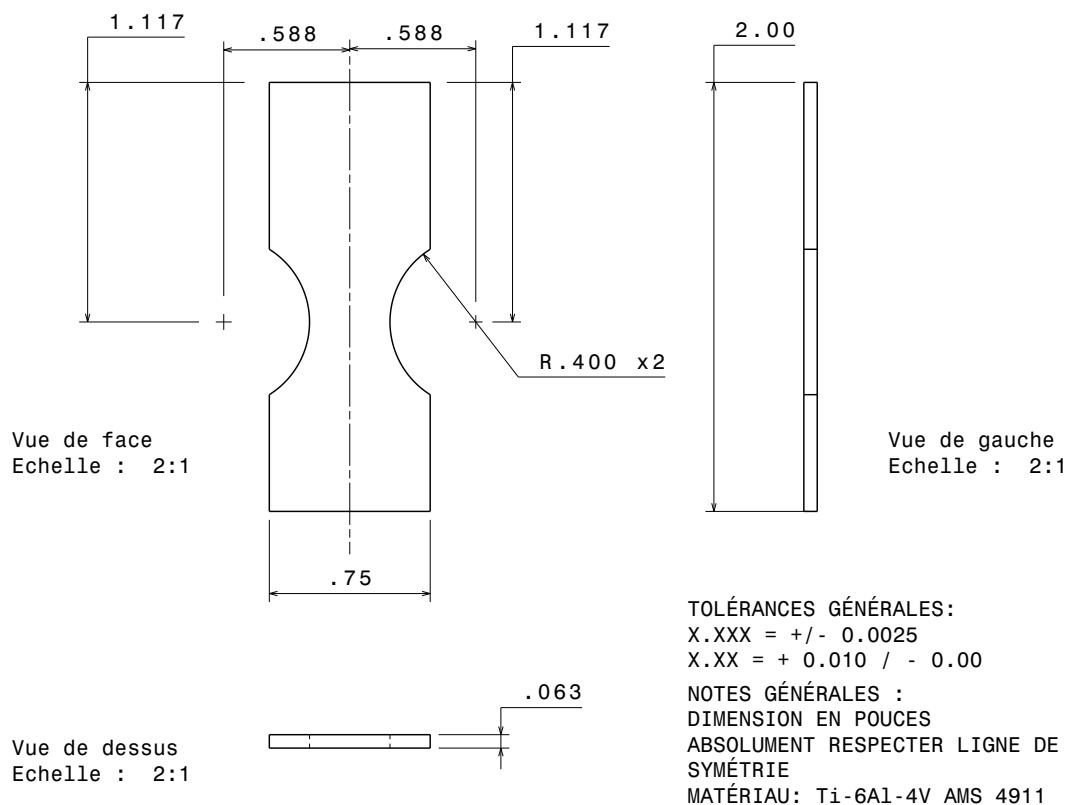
Dessin de fabrication des spécimens utilisés pour les essais de fatigue
